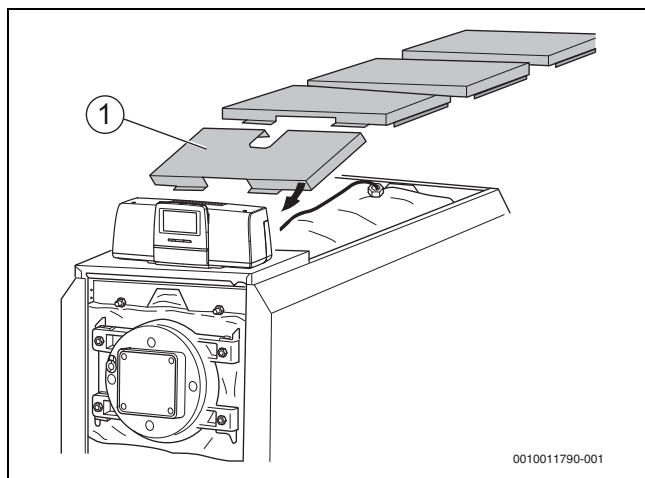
Установка частей верхней крышки котла — принципиальная схема
